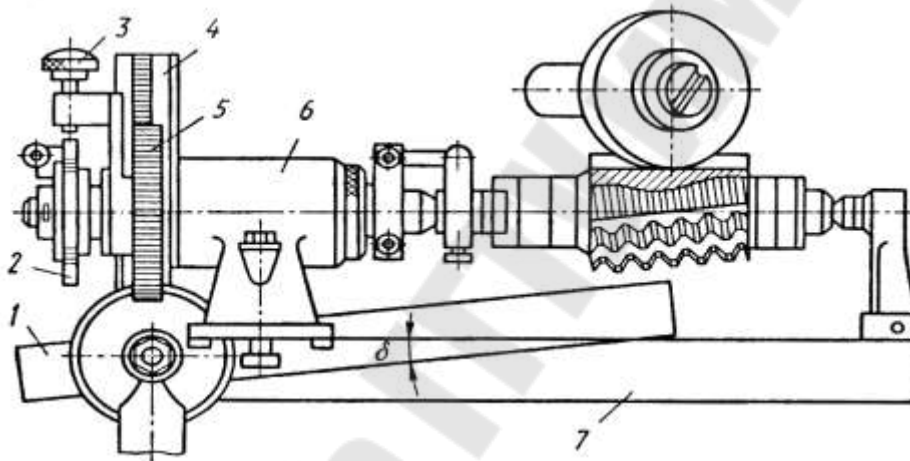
Эскиз приспособления для заточки червячных фрез на универсально-заточном станке: 1 – копирная линейка; 2 – делительный диск; 3 – фиксатор; 4 - рейка; 5 – шестерня; 6 – бабка изделия; 7 – стол станка
